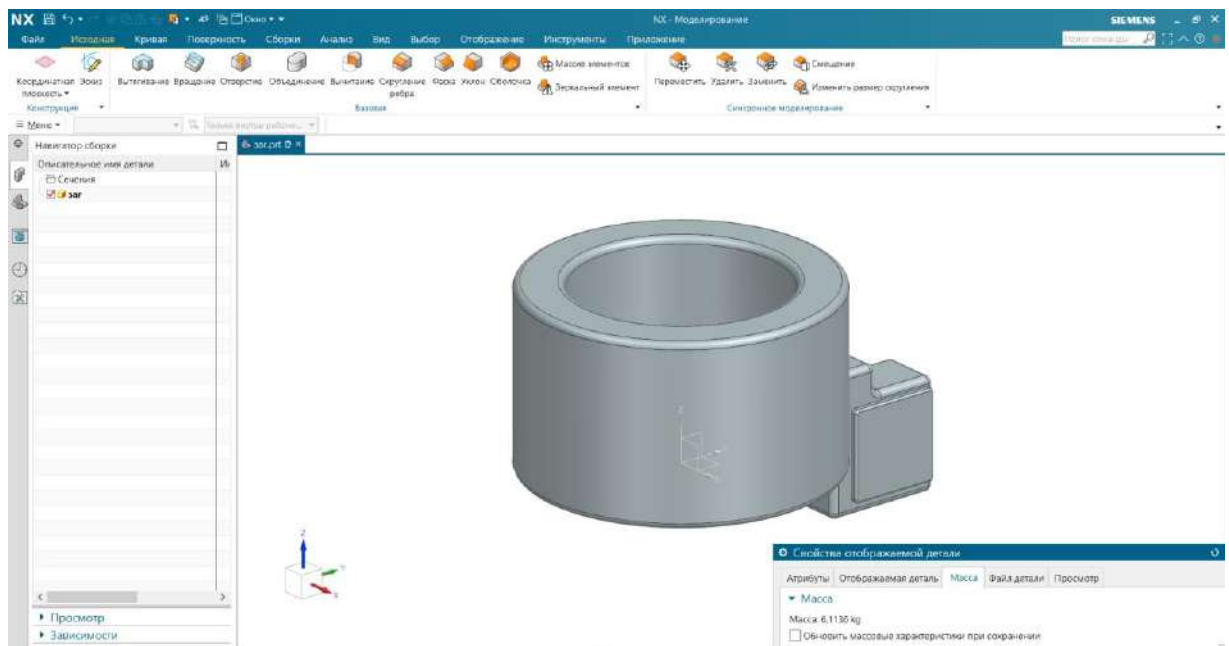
Заготовка, що отримується литтям в кокіль
